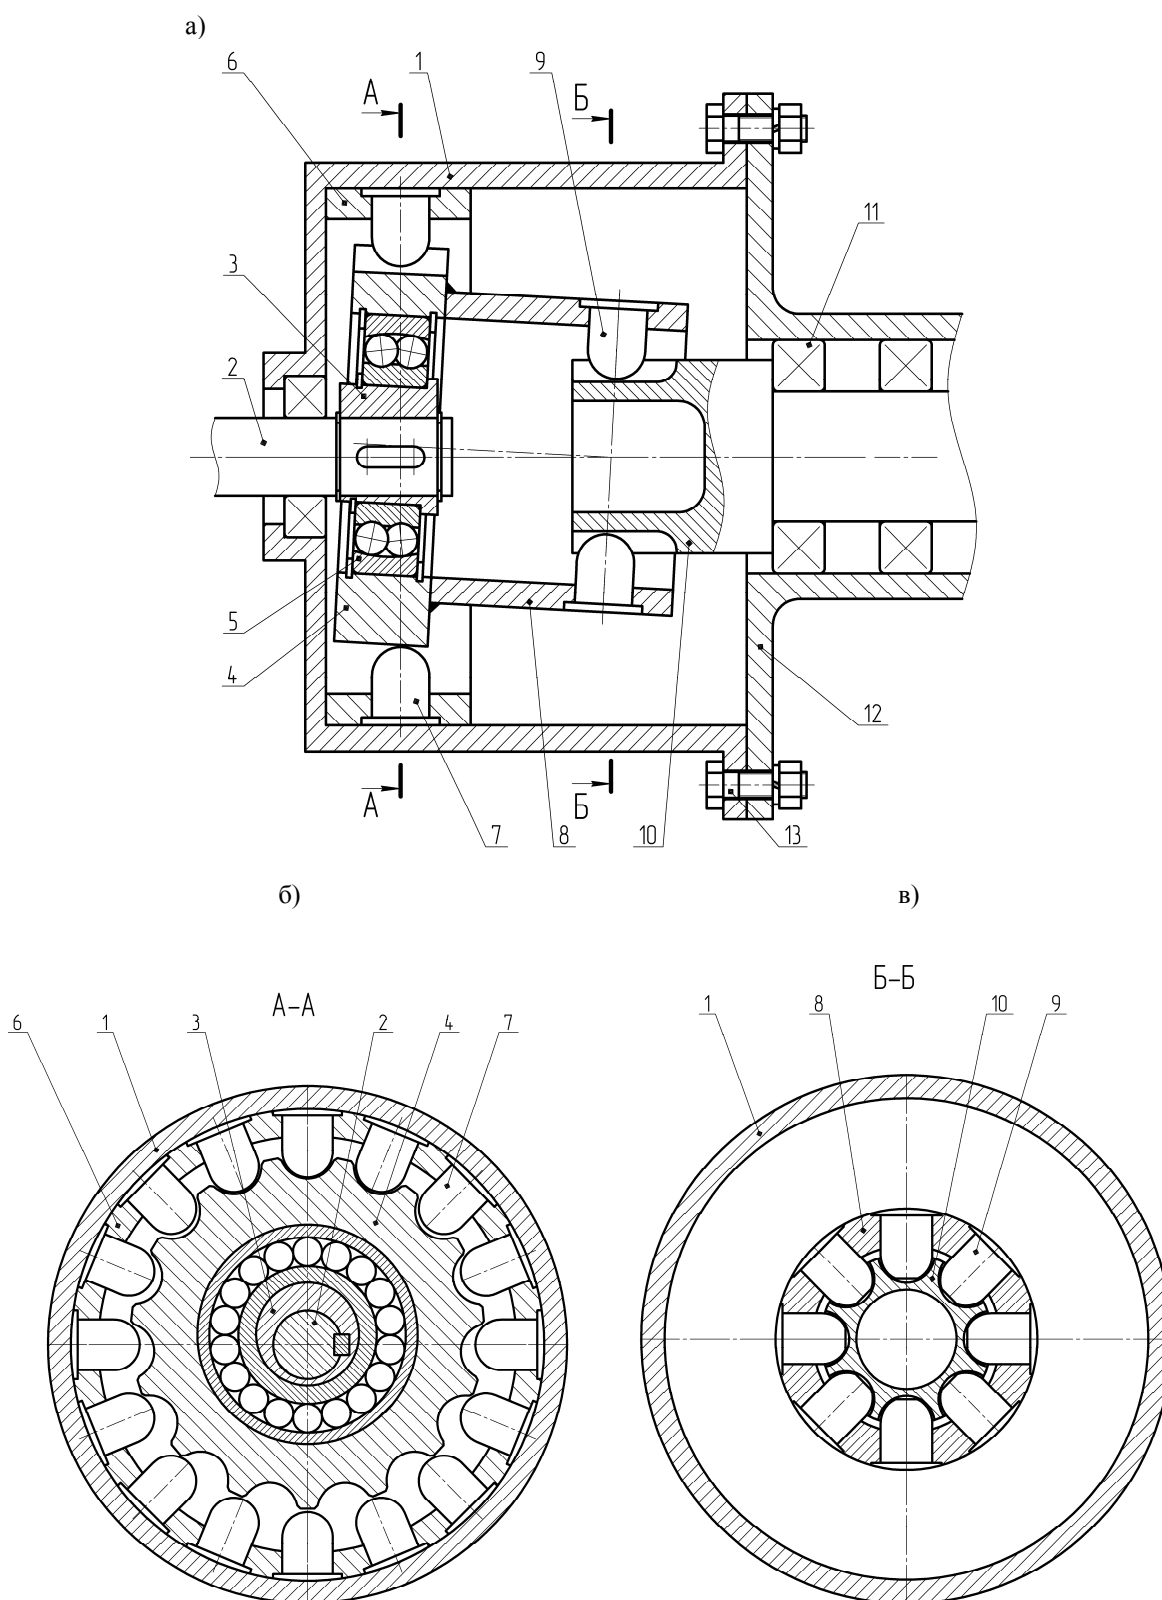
Структурная схема планетарной прецессионной передачи с радиальными сферическими пальцами: а – с соосным расположением входного и выходного валов; б – сечение А-А; в – сечение Б-Б; 1 – корпус; 2 – входной вал; 3 – косая втулка; 4 – сателлит; 5 – сферический подшипник; 6 – неподвижное центральное колесо; 7, 9 – сферические пальцы; 8 – кольцо; 10 – выходной вал; 11 – подшипниковая опора; 12 – корпус привода; 13 – болтовое соединение
